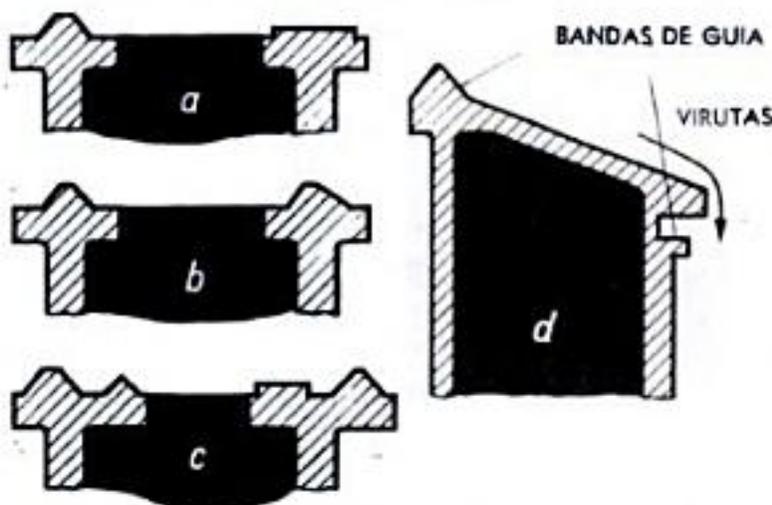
,2 Disposición de las guías: a) Una banda de guía prismática y la otra plana; b) ambas bandas de guía prismáticas; c) bandas de guía especiales para el cabezal móvil; d) disposición inclinada de las bandas de guía con objeto de facilitar una ventajosa evacuación de las virutas.
